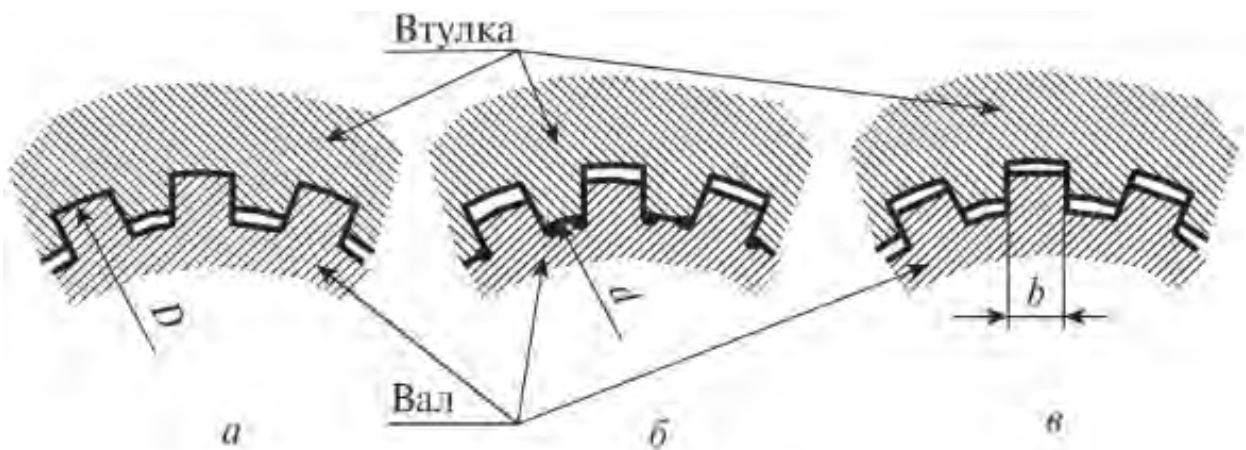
Схемы центрирования шлицевых соединений с прямобочными шлицами:
